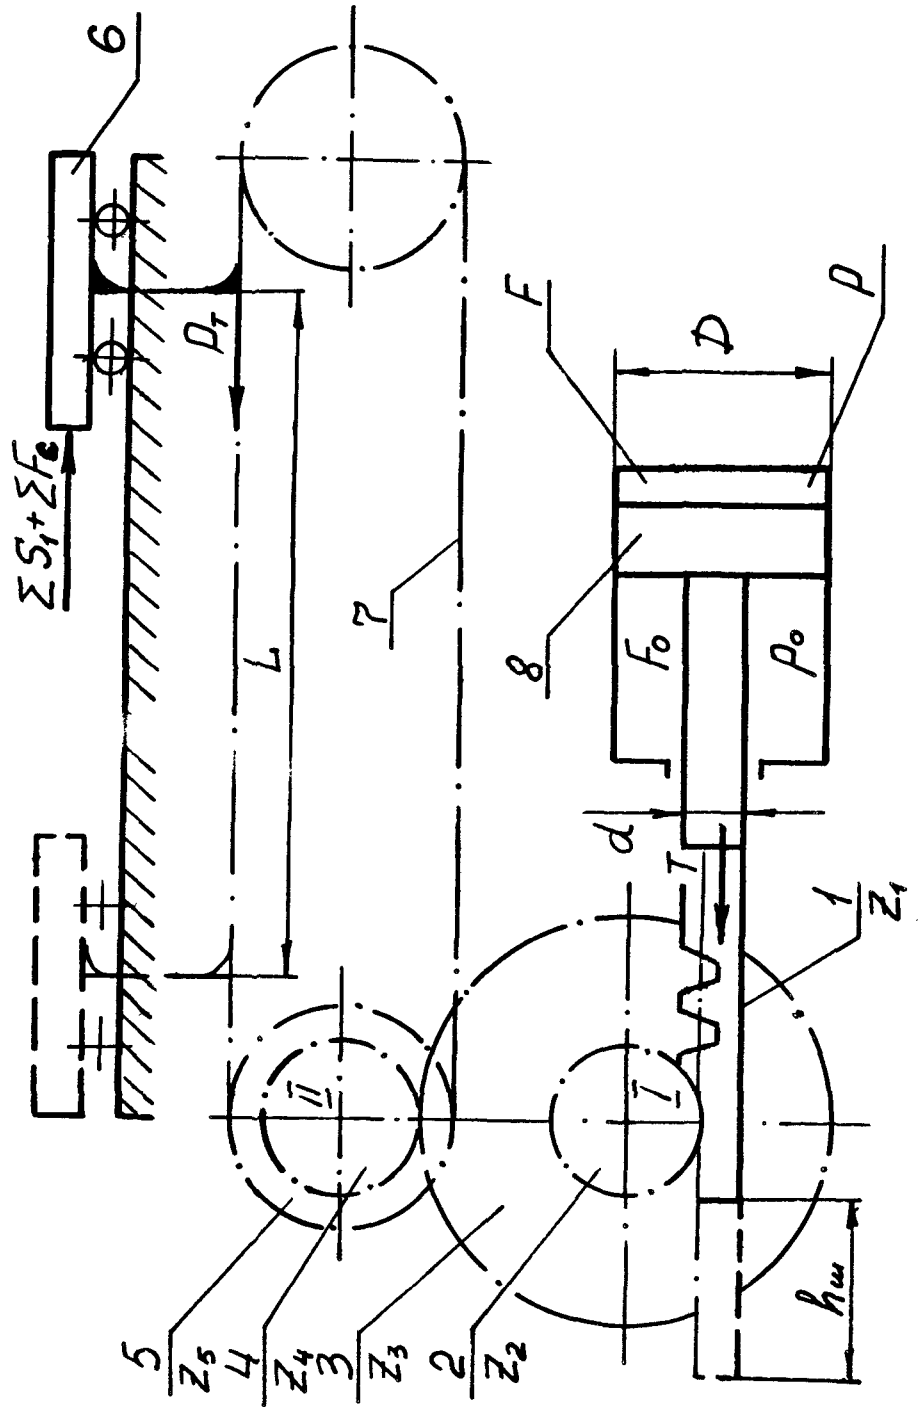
Кинематическая схема механизма подачи заготовки кареткой с приводом от гидродвигателя (станок ШО16-4)
